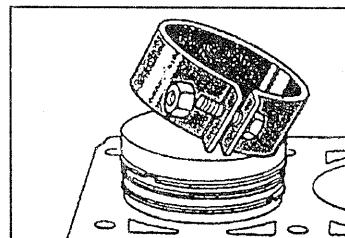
б. Самодельное приспособление для сжатия поршневого кольца
